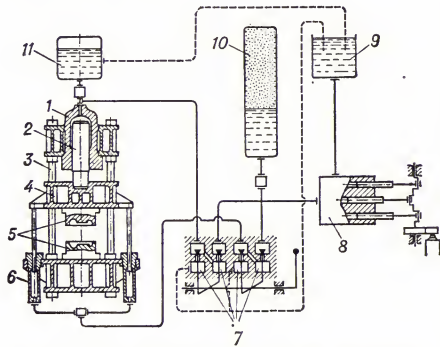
Принципиальная схема гидравлического пресса: 1 — рабочий цилиндр; 2 — плунжер (поршень); 3 — станина; 4 — подвижная поперечина; 5 — инструмент (штамп); 6 — цилиндр обратного хода; 7 — клапаны управления; 8 — насос; 9 — сливной бак; 10 — воздушно-гидравлический аккумулятор; 11 — дополнительный бак.
